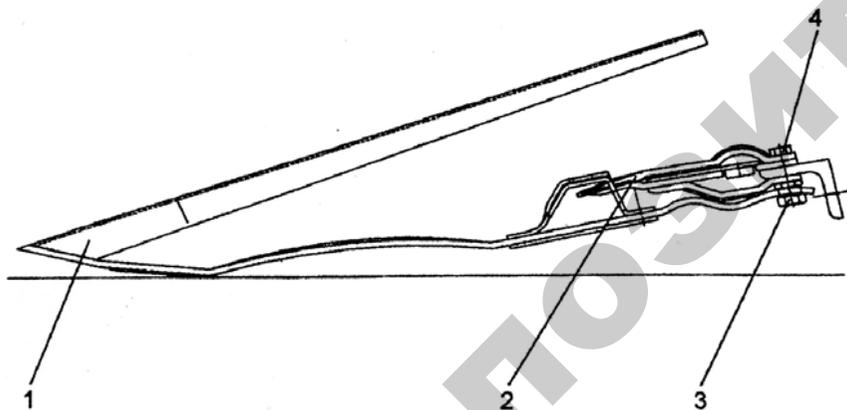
Установка стеблеподъемника: 1 — стеблеподъемник; 2 — палец режущего аппарата; 3 — гайка; 4 — болт
